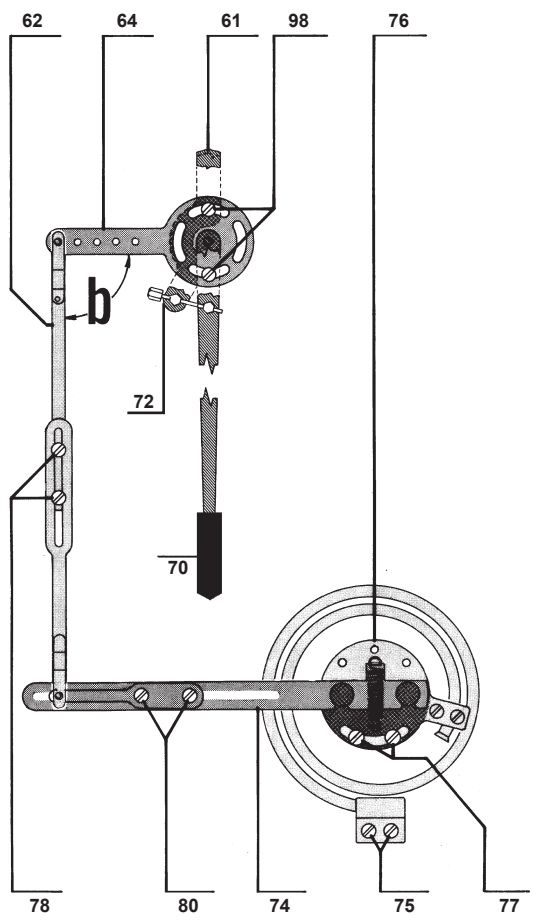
Elemento di misura con molla a spirale (manometrica o termometrica)
